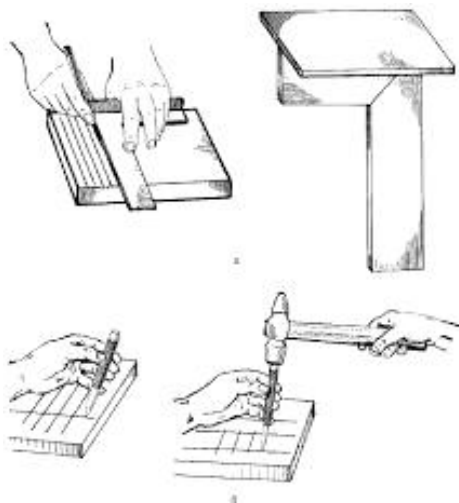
Нанесення та накернювання розмічувальних рисок
